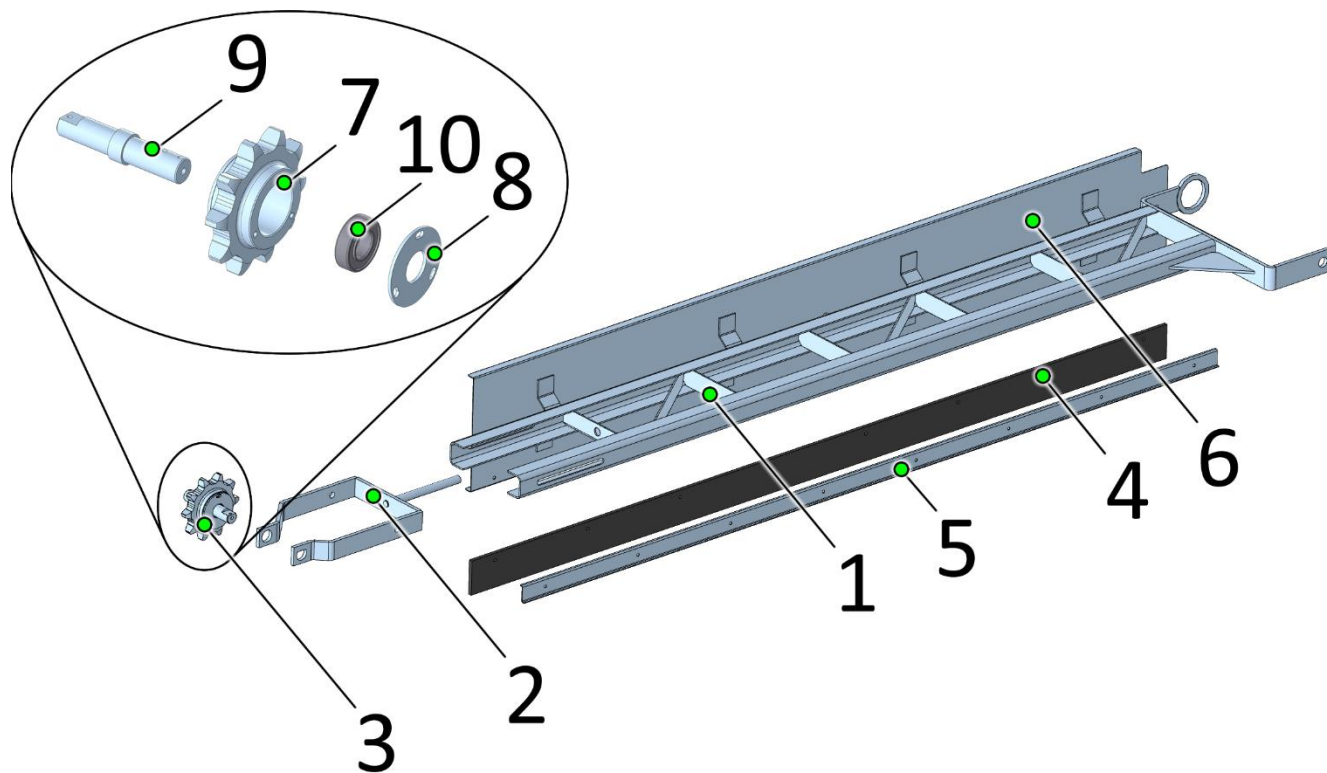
Питатель \_ ЗСК-02.06.000-левый
